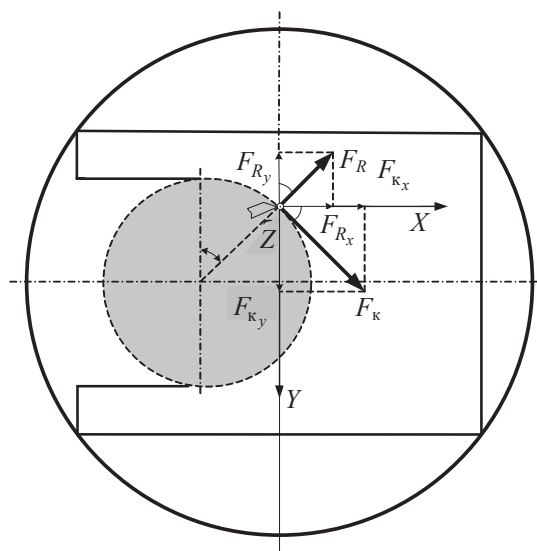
Заготовка, обрабатываемая в пределах базы УДМ-1200
